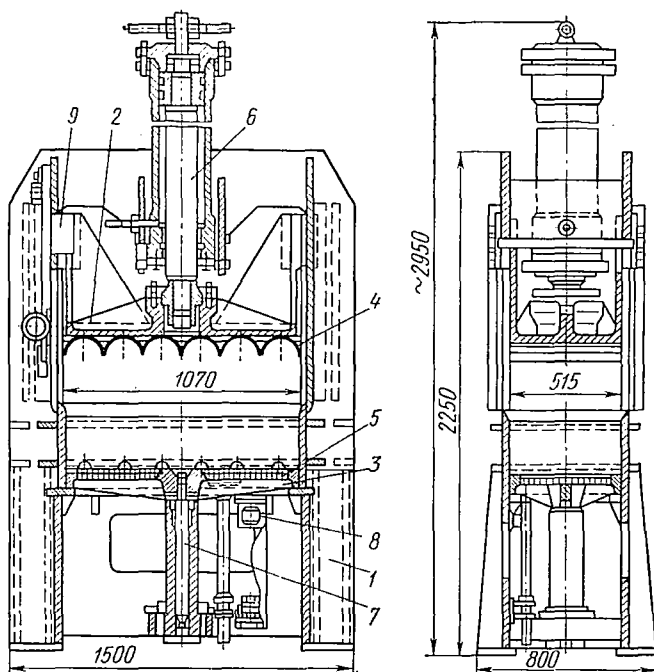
Гидравлический пресс для прессования изделий из перлита и вермикулита
